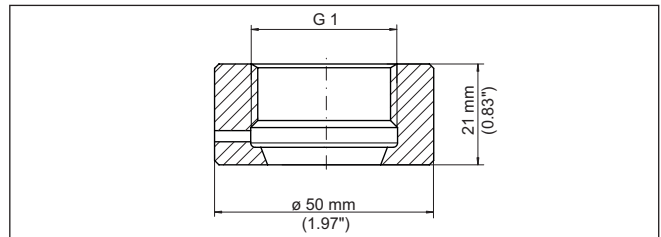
Dimensions raccord à souder direct G1 - joint conique
